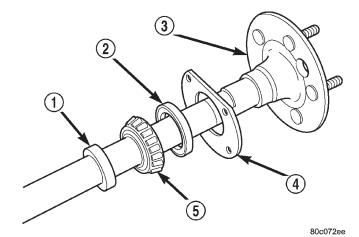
COMPONENTES DEL COJINETE Y LA JUNTA DEL EJE
